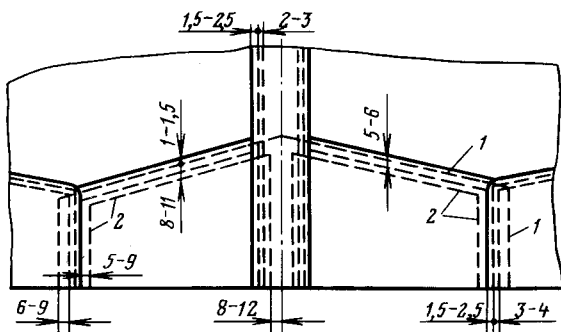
Схема пристрачивания задника в заготовках сапог с верхом из юфти:
